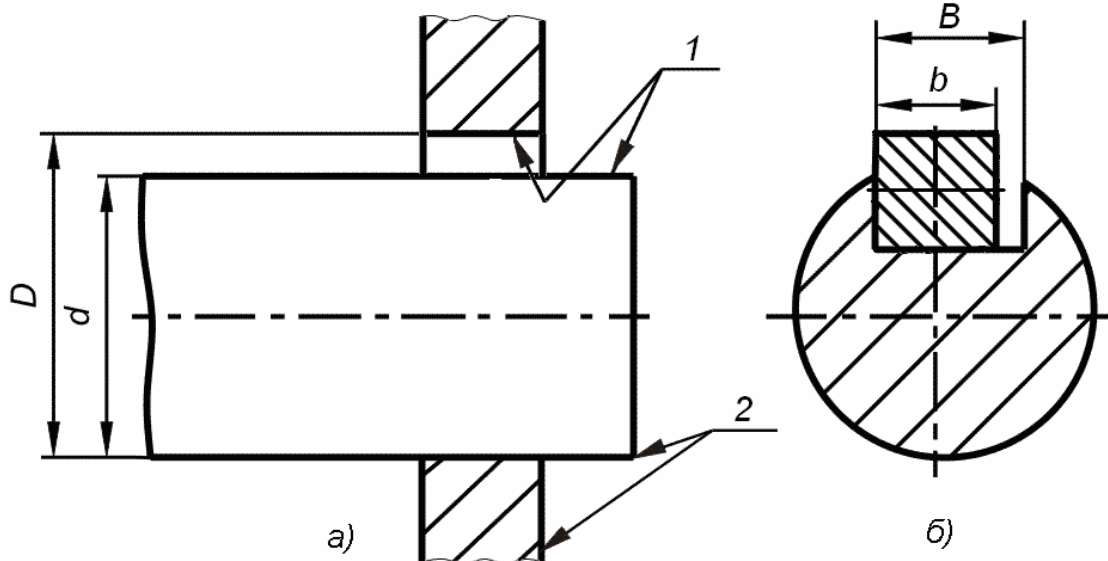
Приклади з'єднань: а – гладкого циліндричного; б – шпонки з пазом вала.
